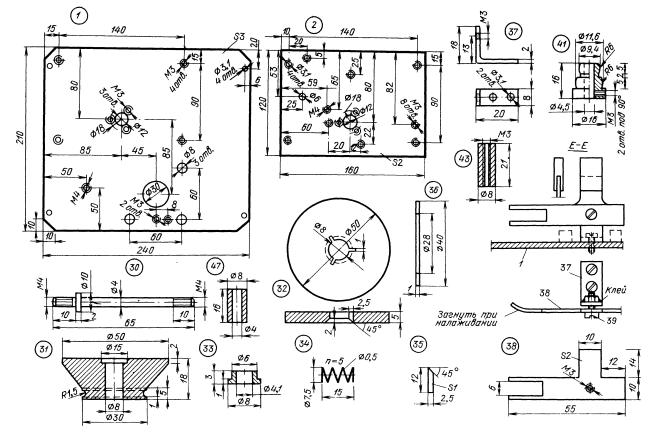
Детали лентопротяжного механизма (рассматривать совместно с рис. 17 и 18)
